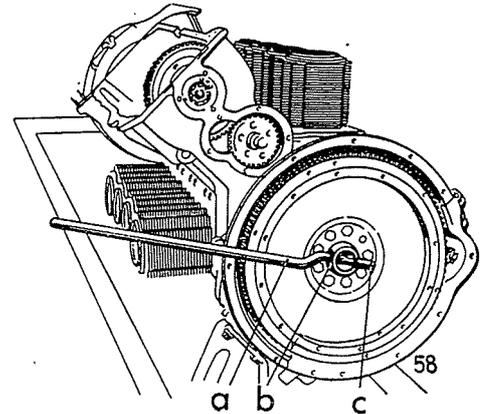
Werkzeug zum Durchdrehen der Kurbelwelle
